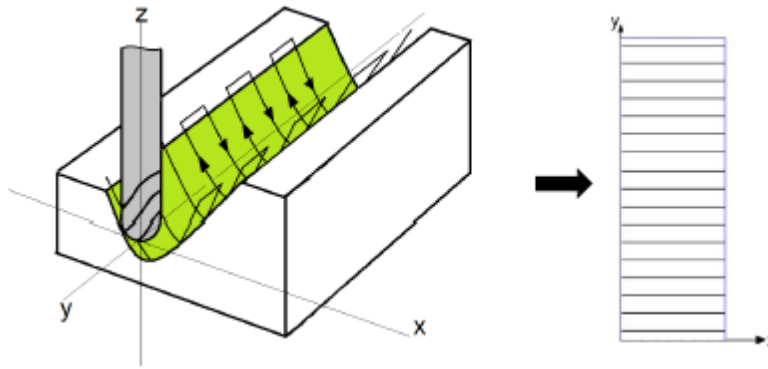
Схема фрезерування з траєкторією, розташованою поперек формуючої поверхні
